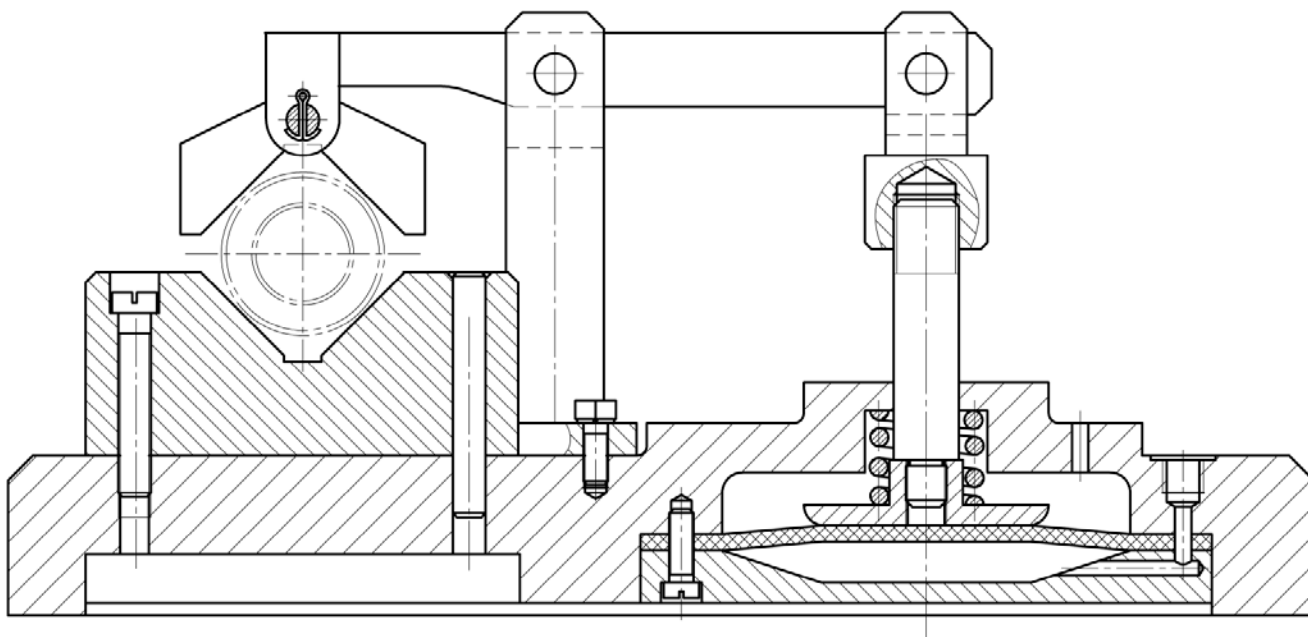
Компоновка (общий вид) приспособления показан на чертеже.
